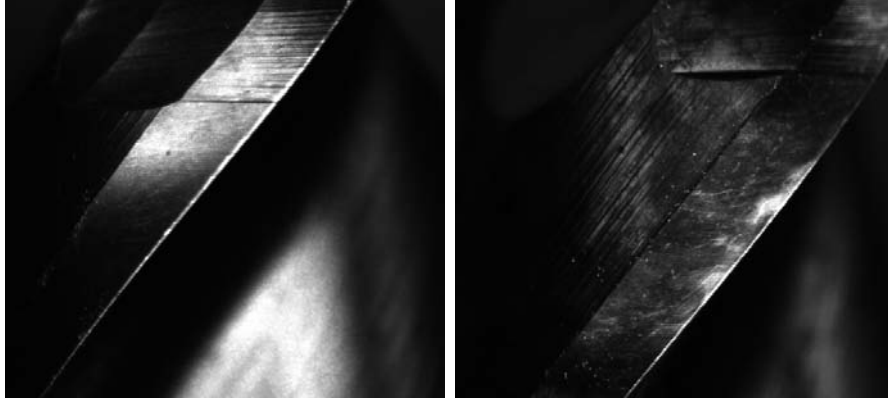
Comparaison de l'usure en dépouille d'un carbure MG12 et d'un carbure EMT100 après fraisage d'un alliage d'aluminium silicium
